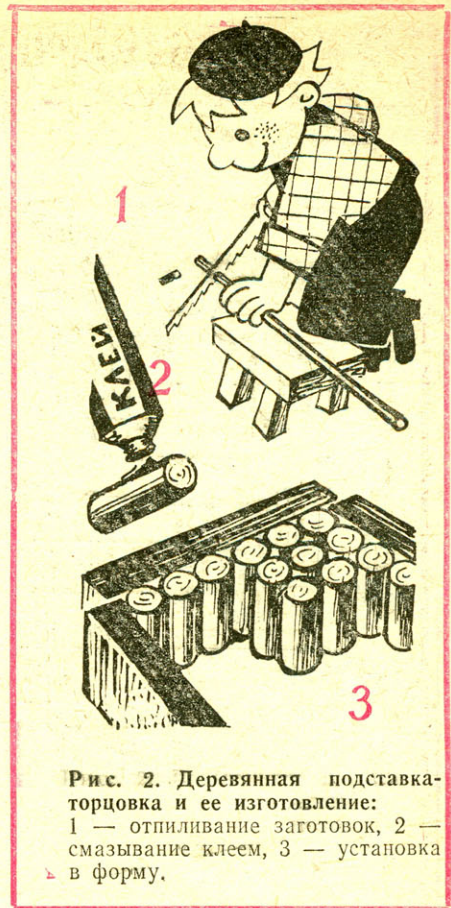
Деревянная подставка-торцовка и ее изготовление:
